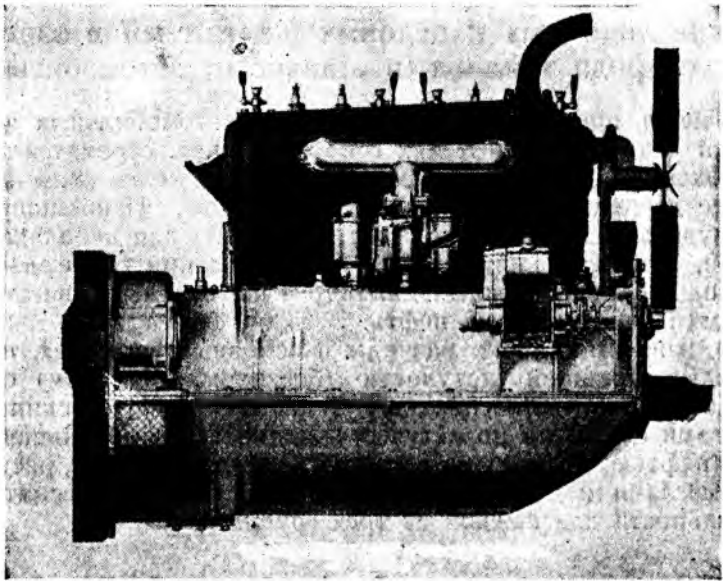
Общий вид карбюратора, установленного на четырехцилиндровом двигателе лодочного (или тяжелого автомобильного типа) Двигатель 4-х цилиндровый. Карбюратор ясно выделяется на темном фоне отливки; вверх идет разветвляющаяся всасывающая труба.
